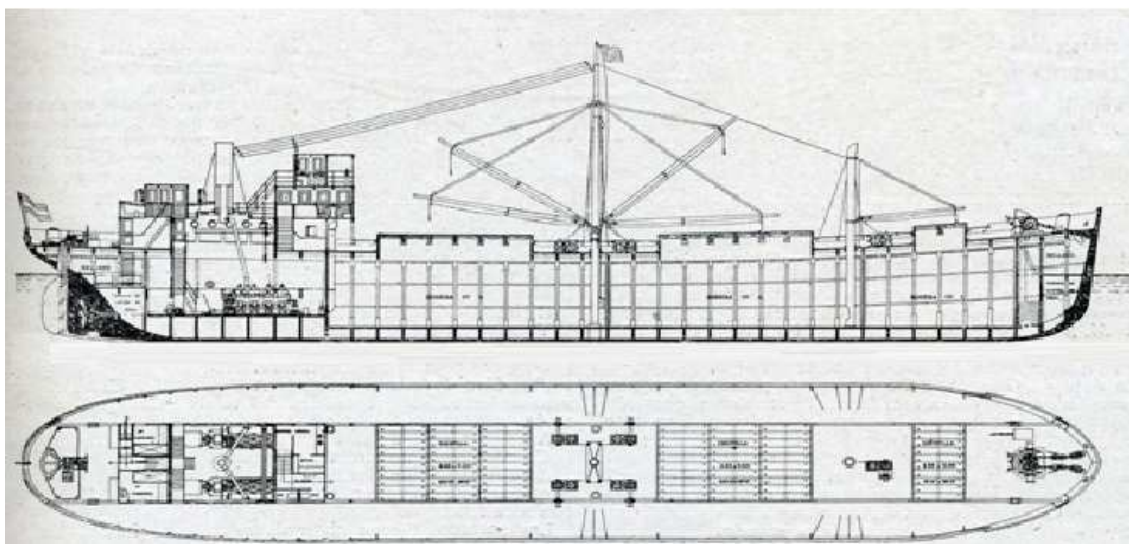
Planos de los buques proyectados por la compañía Construcciones y Pavimentos S.A. (www.vidamaritima.com).
